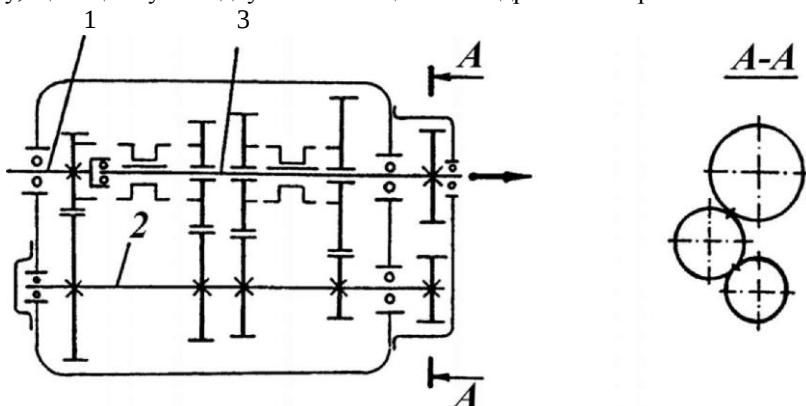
Принципова схема тривальної коробки передач.
